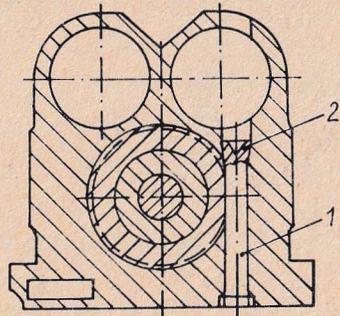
Einbau des Sicherungsbolzens in den Verschlusskörper
